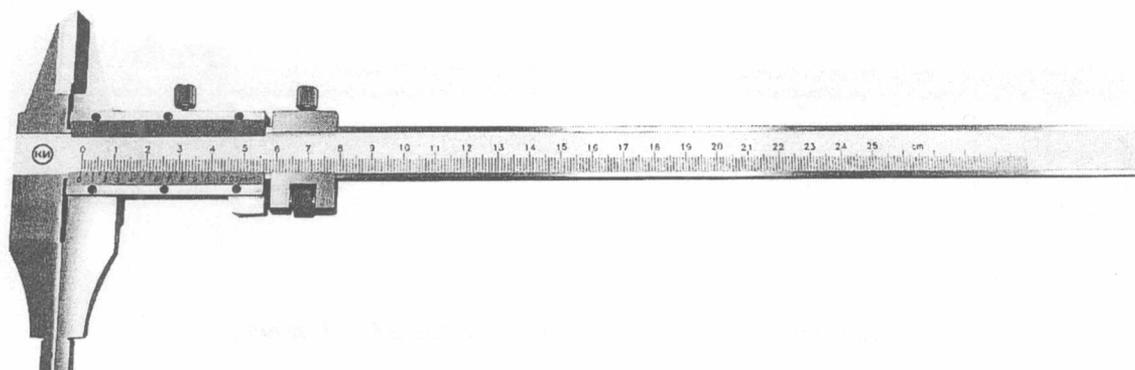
Общий вид штангенциркулей типа ШЦ-II
